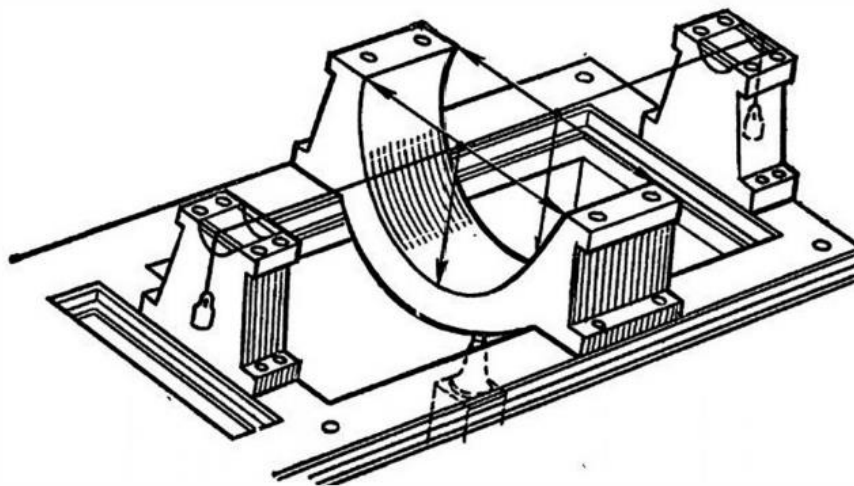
Выверка подшипниковых стоек и станины двигателя
